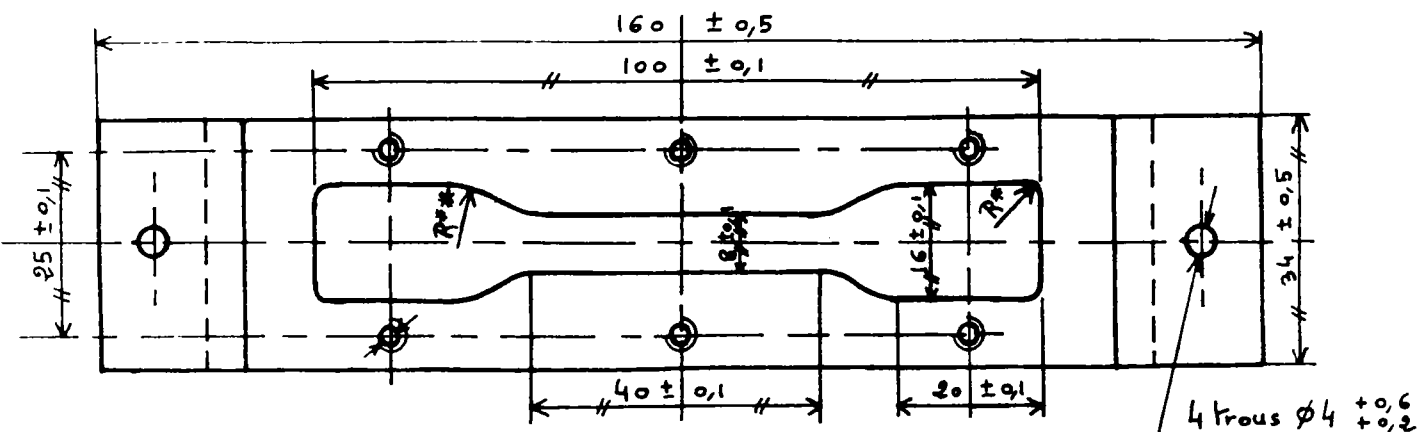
Moule de traction servant à la fabrication des éprouvettes en colle massive.
